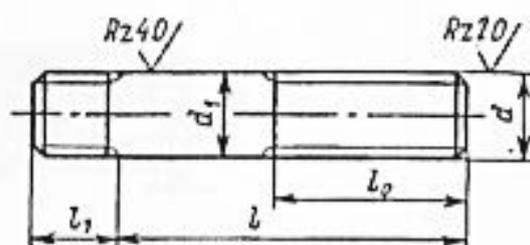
Шпильки общего применения повышенной точности для деталей с резьбовыми отверстиями
